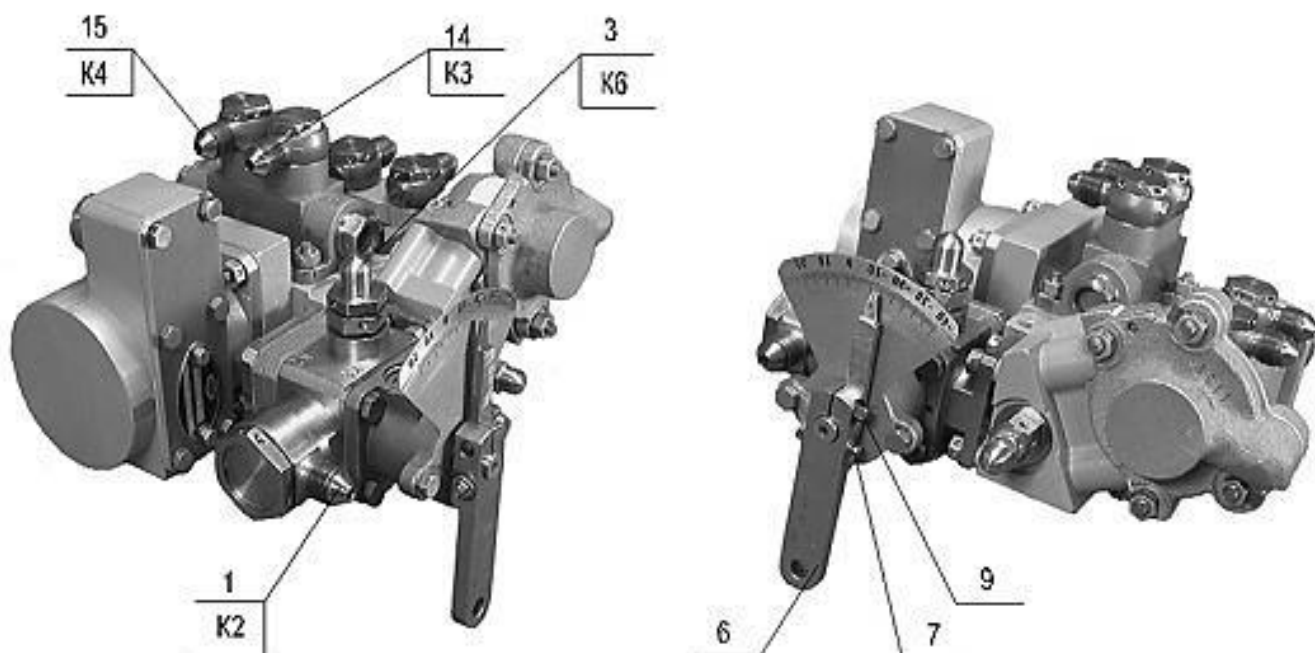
Агрегат управления направляющими аппаратами компрессора АУНАК-157ВР
